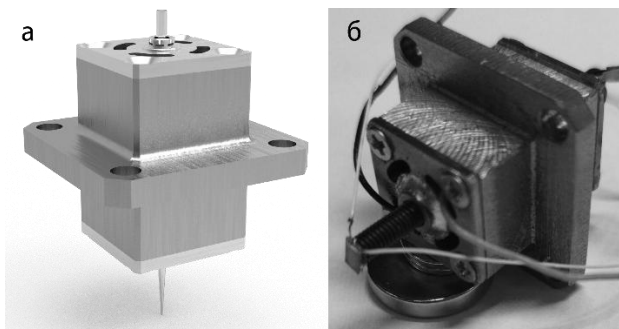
Лабораторный образец сканера модель (а) и изготовленный образец (б)
